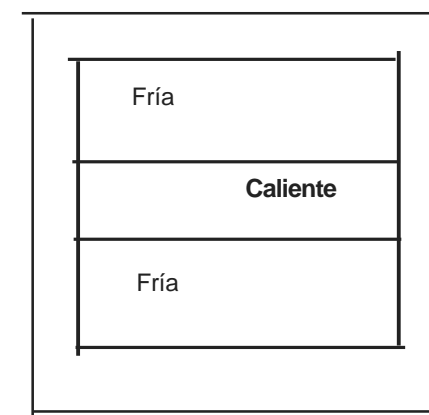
CALENTAMIENTO LOCAL PRODUCIDO DURANTE EL SOLDEO DE DOS CHAPAS
